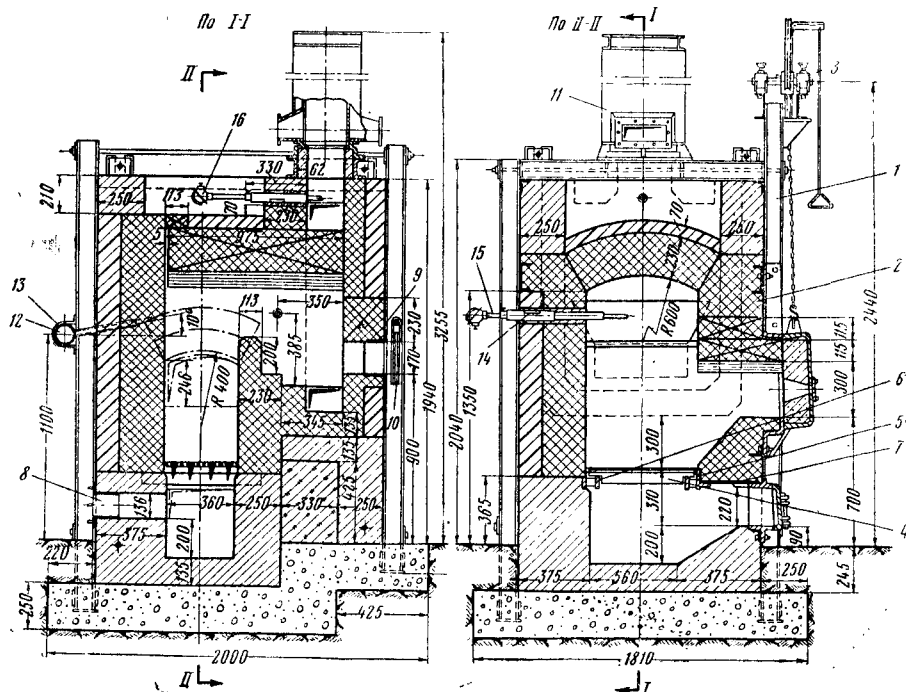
Камерная кузнечная печь (к 0,3 — 0,4-м молоту): 1 — каркас печи; 2 — механизм подъема заслонки топочного окна; 3 — фронт топочного и зольникового окна; 4 — к.с.-ослик плитчатый; 5, 6 — балка подколосниковая; 7 — лист; 8 — патрубок; 9 — коллатор; 10 — фронт рабочего окна; 11 — механизм подъема заслонки рабочего окна; 12 — рекуператор; 13 — горизонтальная установка термометра; 14, 15 — термометра; 16 — сопло для разбавления дымовых газов
